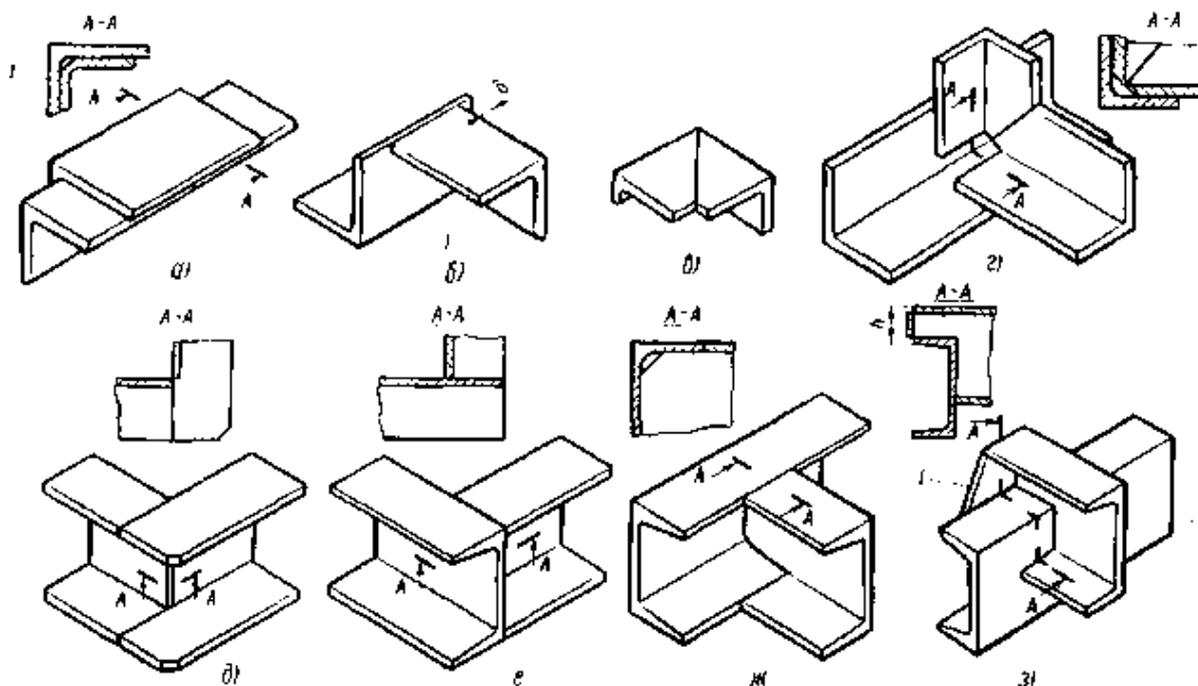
Сопряжения уголков и швеллеров в сварных конструкциях
